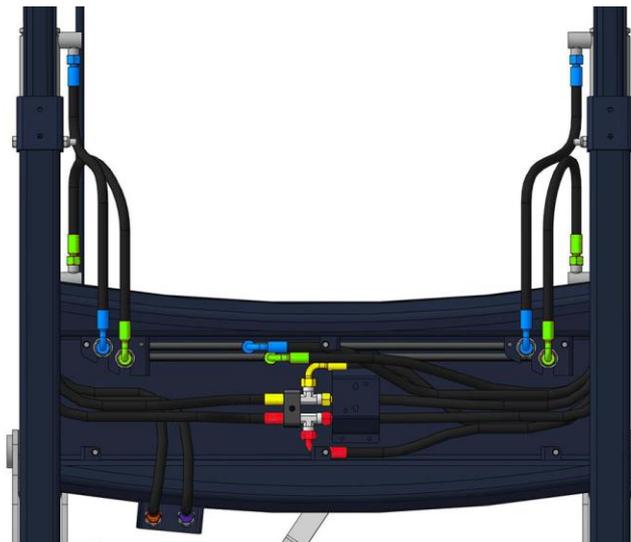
Разводка гидросистемы в поперечной балке
